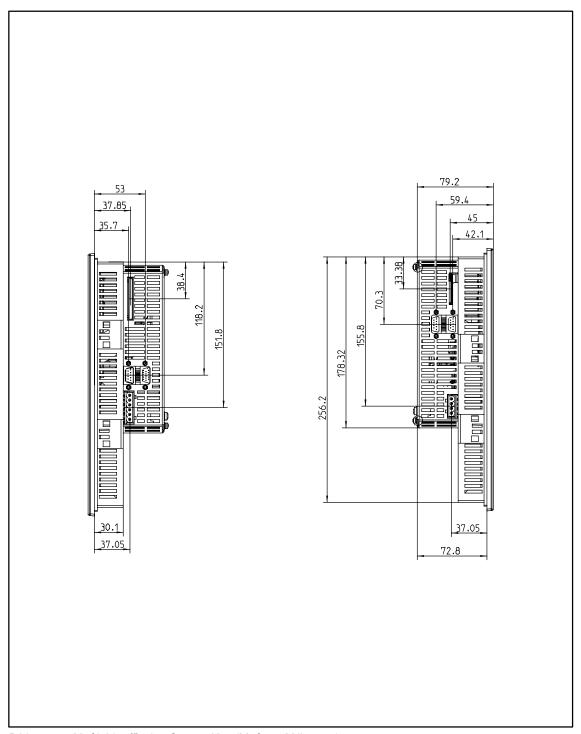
Maßbilder für das C7-635 Key (Maße in Millimeter)
